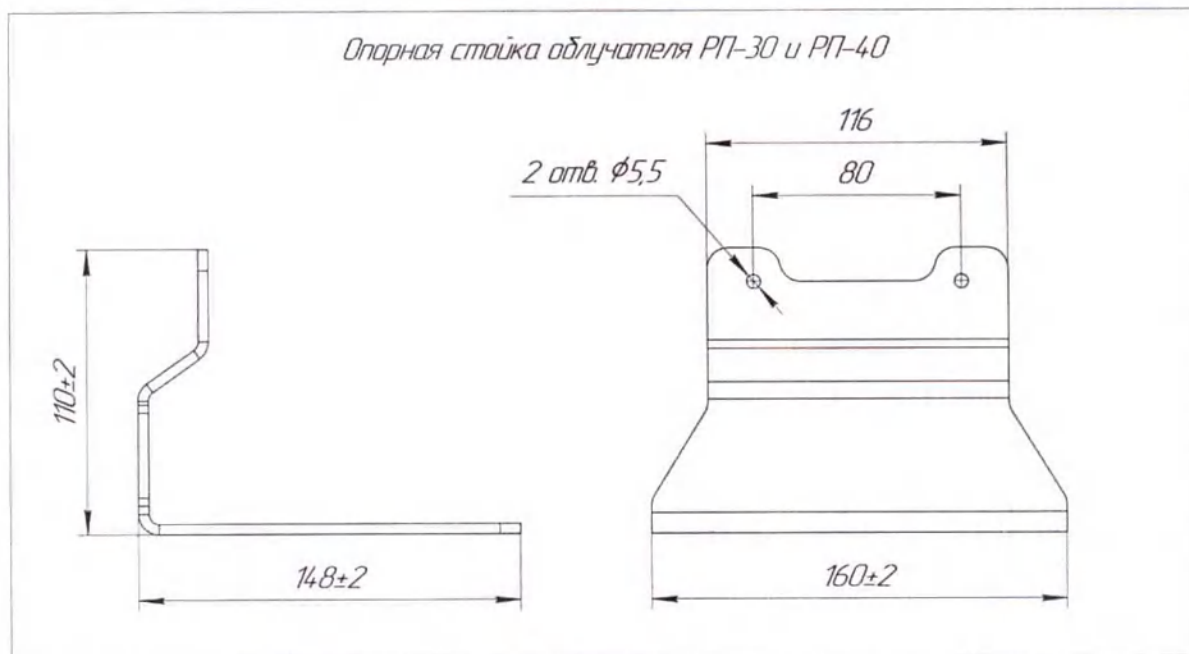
Опорная стойка облучателя РП-30 и РП-40
